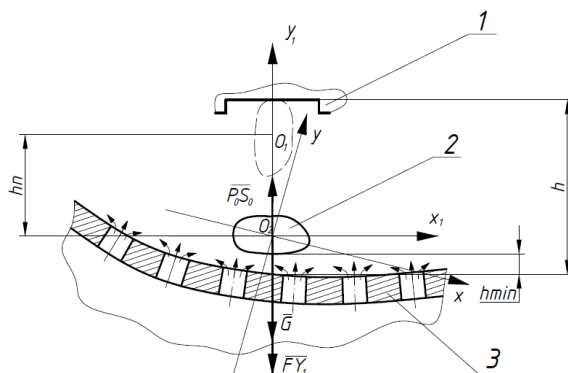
Загрузочный участок конвейера с тонкой воздушной прослойкой для транспортирования нетвердого пищевого полуфабриката: 1 – тестовая заготовка; 2 – несущая поверхность пневмоустановки.
